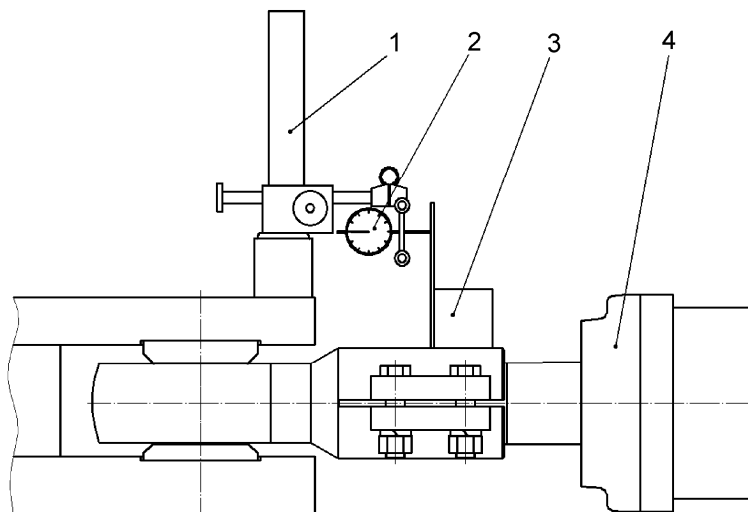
Измерение радиального люфта в шарнирах цилиндров поворота (крепление к поворотным рычагам):
